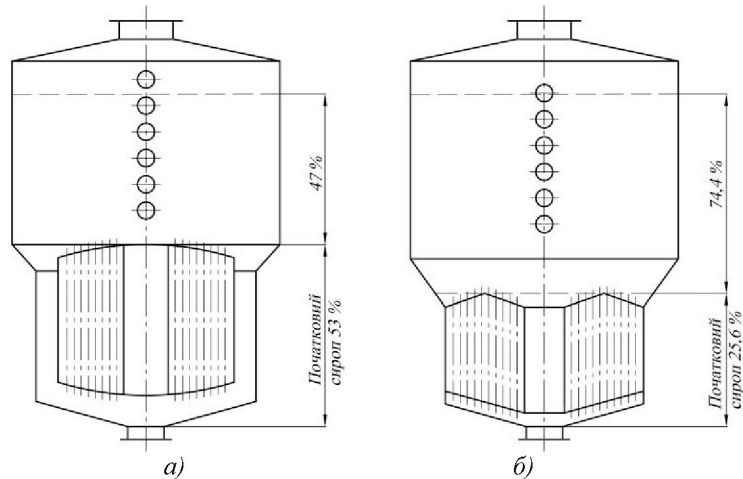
Схеми конструкцій вакуум-апаратів: а) ВМА-600; б) ВАМЦ-600.
